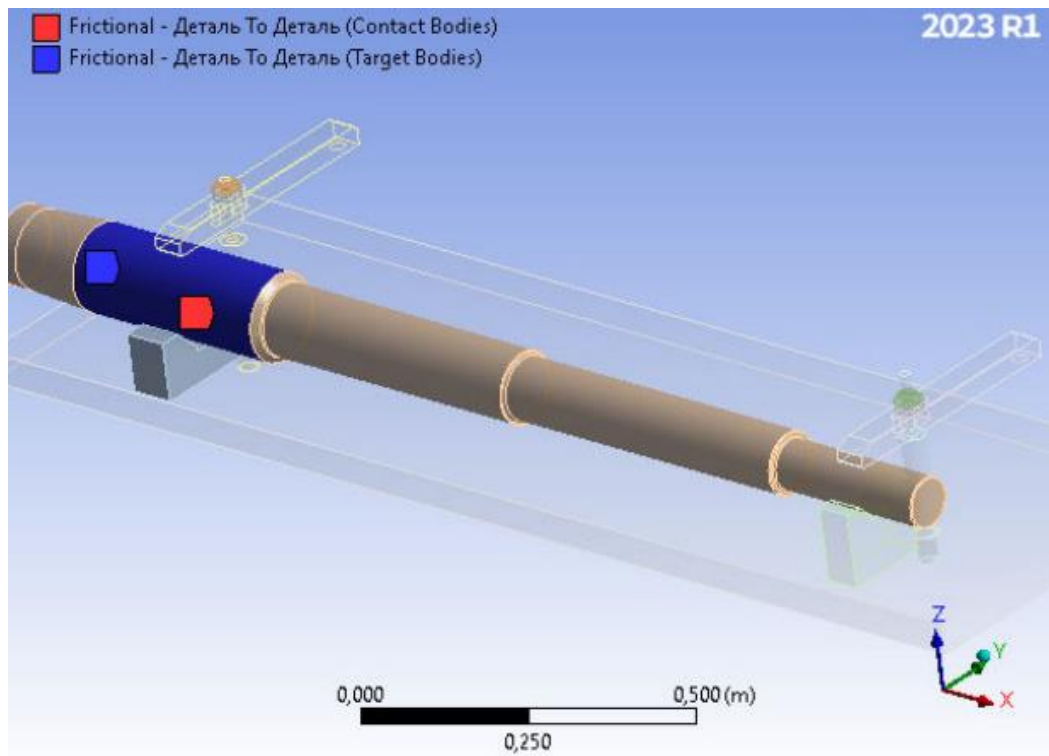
Характеристика контакту сполучених поверхонь «заготовка-призма»
